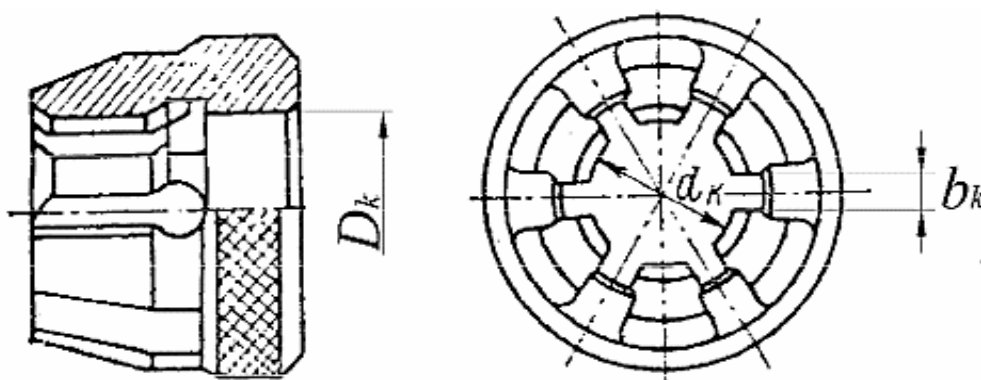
Калибр для контроля расположения наружной шлицевой поверхности
